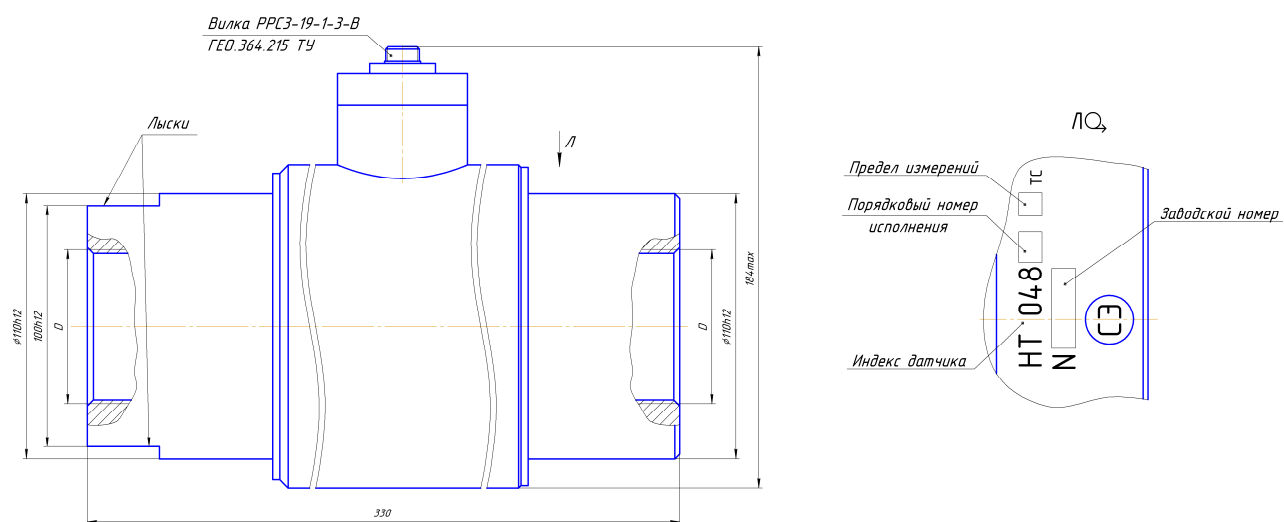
Габаритно-установочные размеры датчика НТ 048
